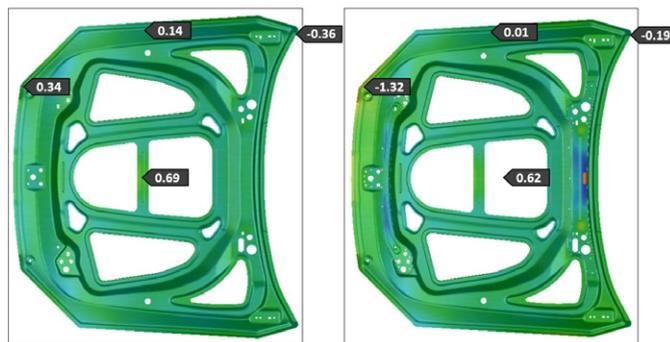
Springback* Capô Interno Compensado e do Conjunto Soldado
